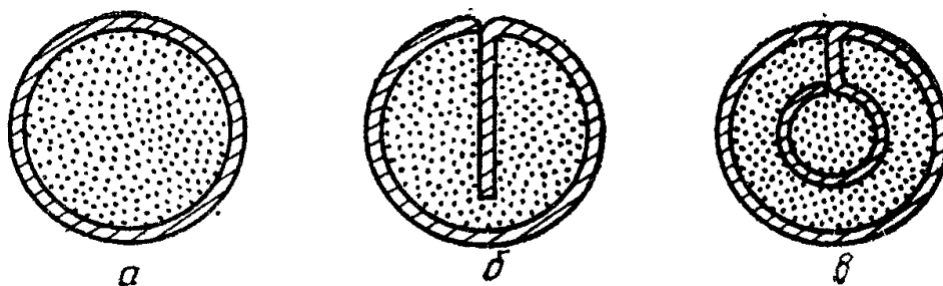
Номенклатура зварювального порошкового дроту
